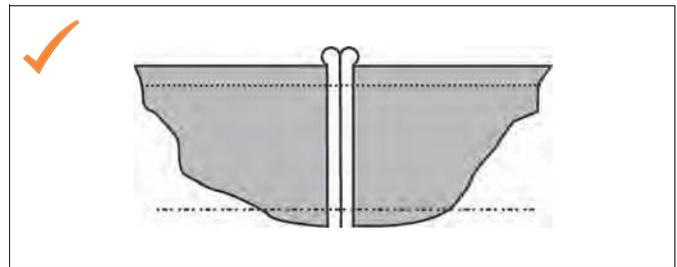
Schweißnaht mit zu großen Wülsten (gut bis ausreichend)
